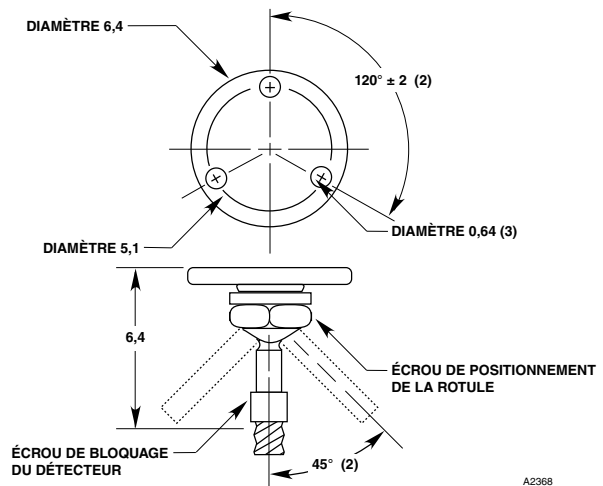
Dimensions du Support de Montage à Rotule en Aluminium Q9001A (en Centimètres)
